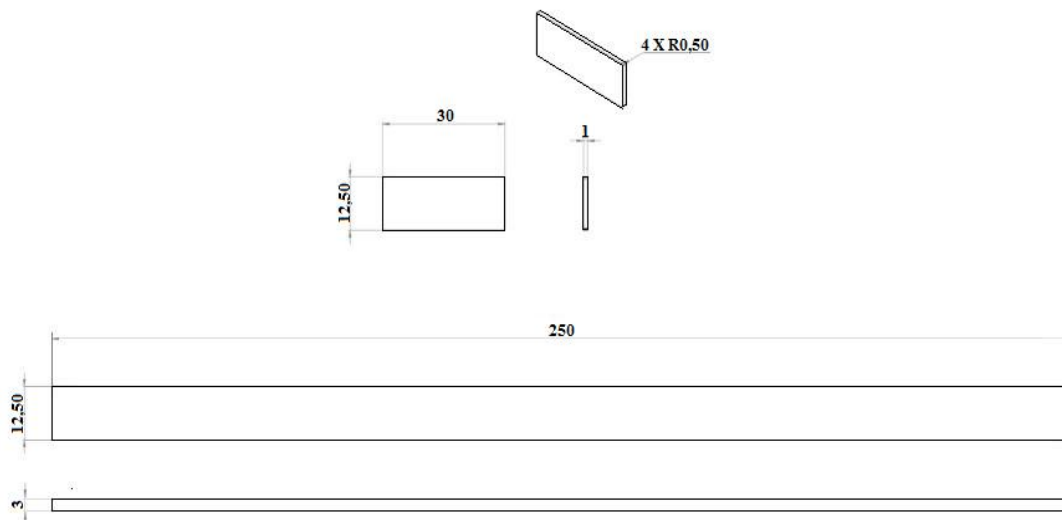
Dimensões da barra e chapa de alumínio (em mm).
